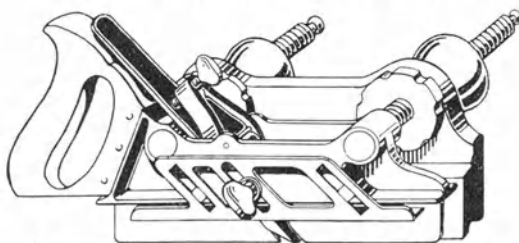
Nuthobel mit eisernem Gehäuse (Wien. Patent).
